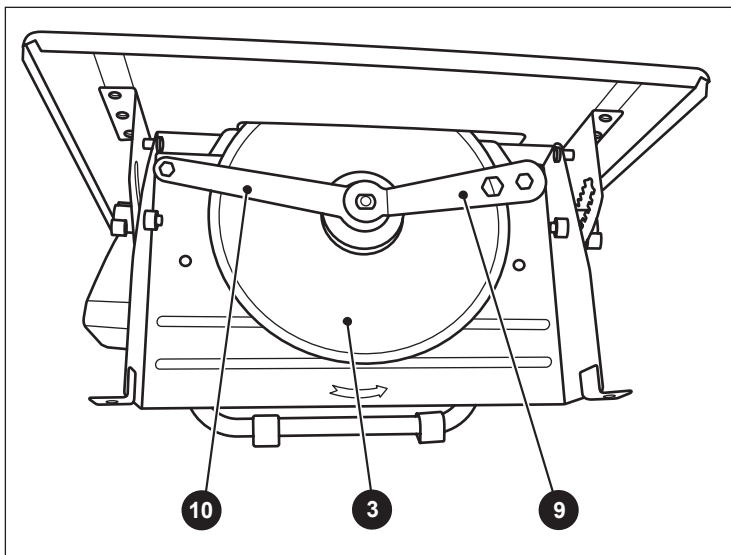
Рисунок G – установка і кріплення алмазного диска на шпindelі верстата.
